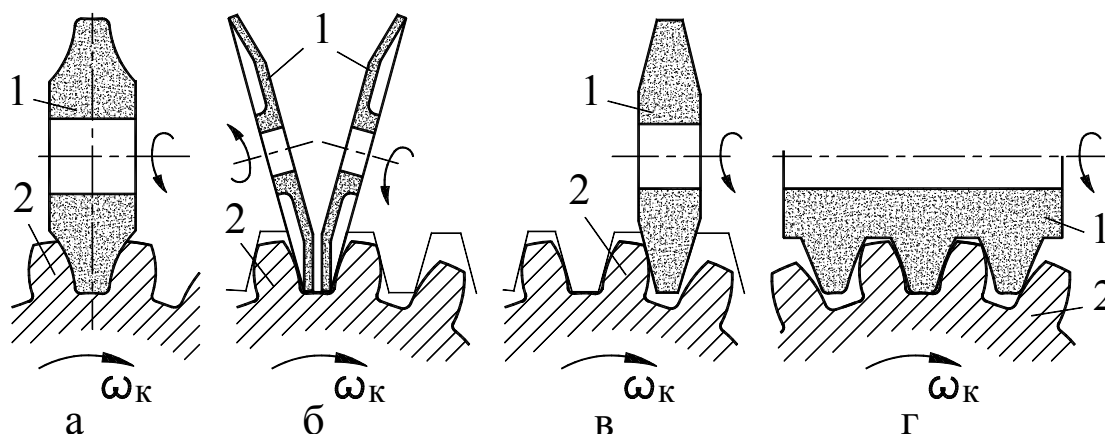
Методы шлифования зубьев колес: а – копирования, б, в, г – обкатывание с помощью двух тарельчатых кругов, дискового круга, червячного круга, соответственно; 1 – инструмент; 2 – обрабатываемое колесо; ω_k – направление движения колеса
